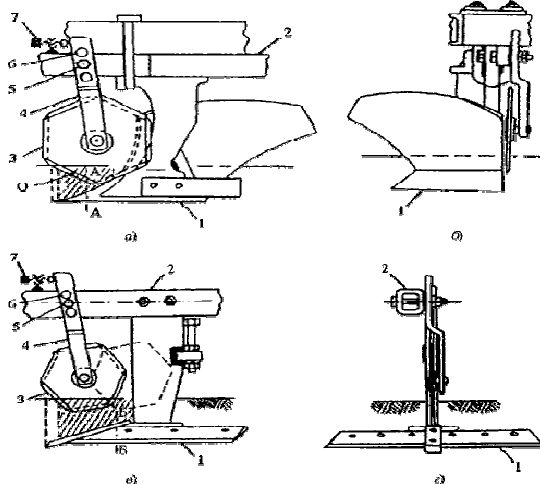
Рабочий корпус плуга (а, б) и плоскореза (в, г): а, в – вид слева; б, г – вид спереди
